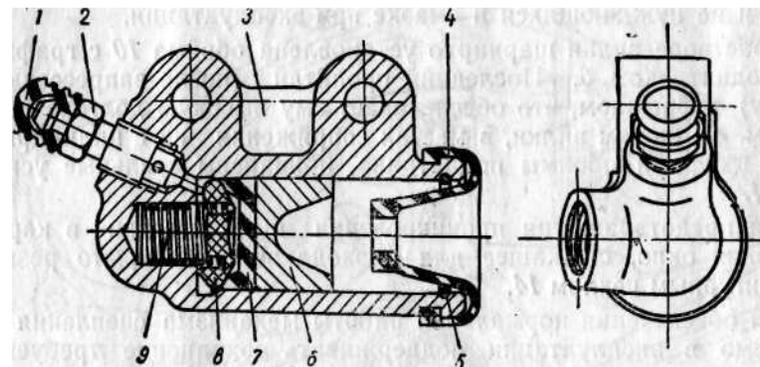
Рабочий цилиндр гидропривода выключения сцепления:
